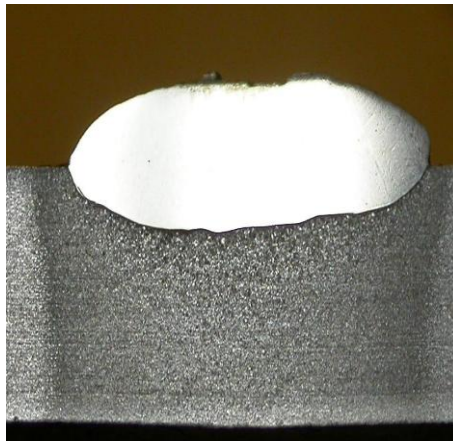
Muestra 4 usando soldadura FCAW con electrodo autoprotegido
